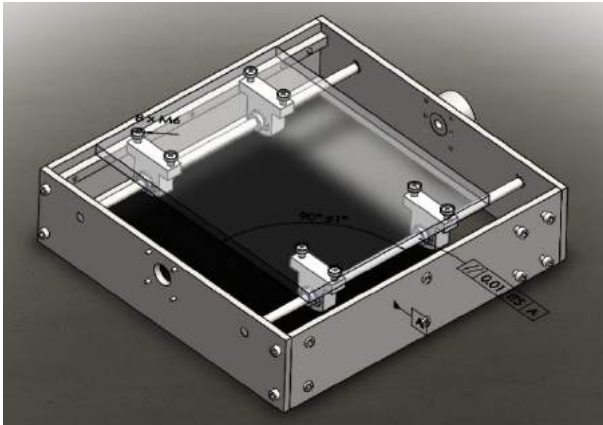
Tolerancias geométricas en mesa de trabajo
